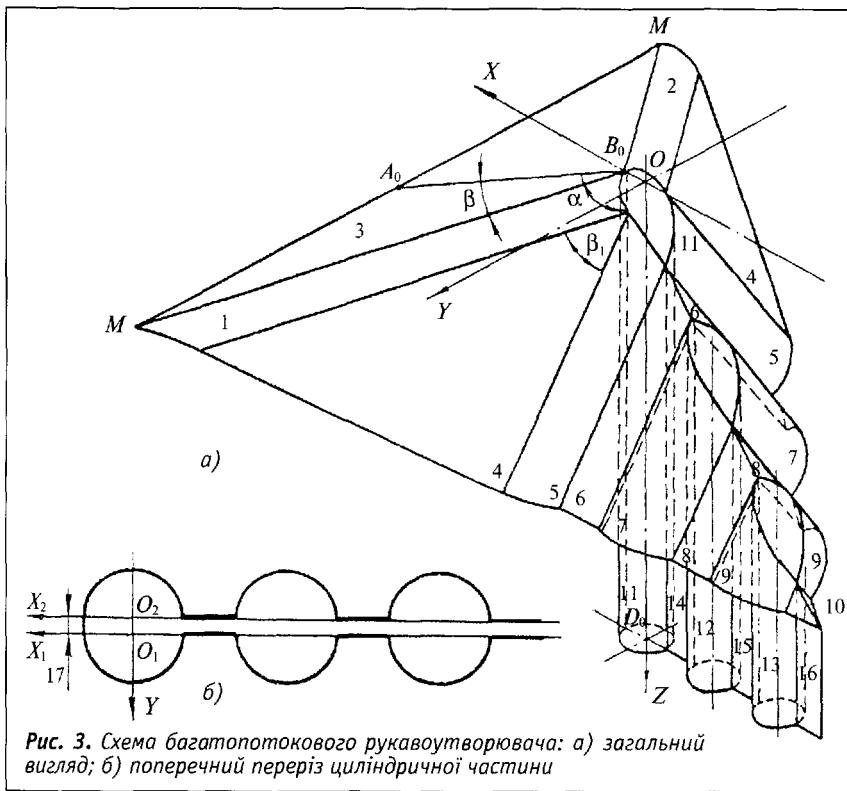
Схема багатопотокового рукавоутворювача: а) загальний вигляд; б) поперечний переріз циліндричної частини
